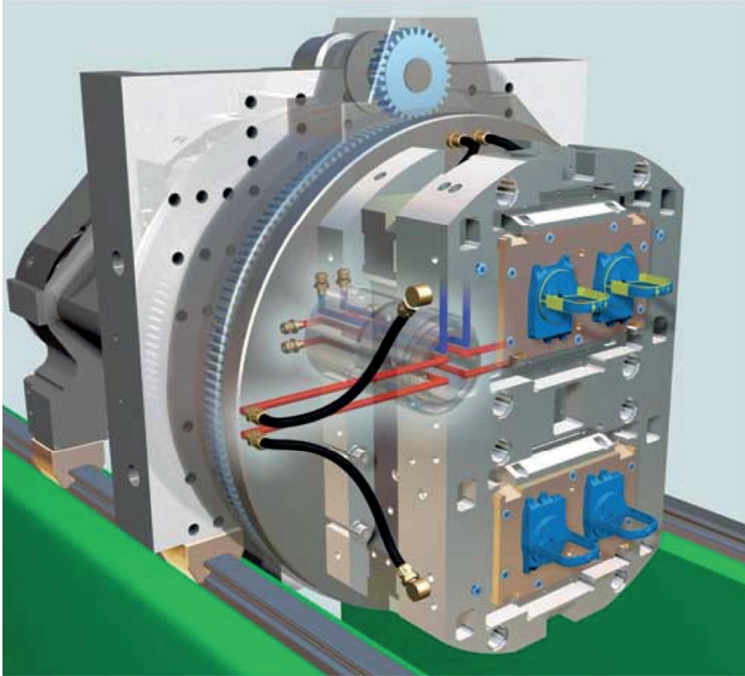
Beispiel eines Spritzgießwerkzeugs mit Rotation um die horizontale Achse
